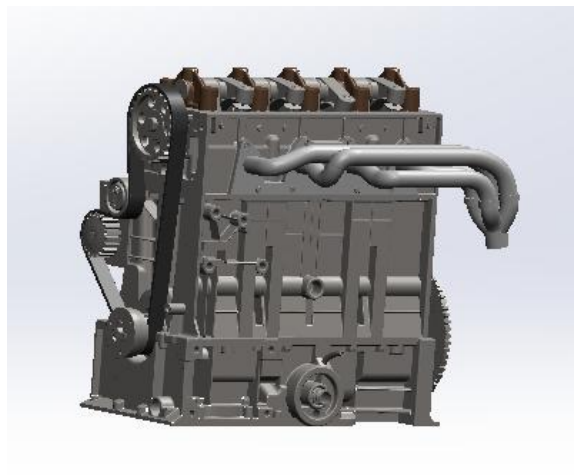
Motor 4 cilindros en línea. Ref. [3]
